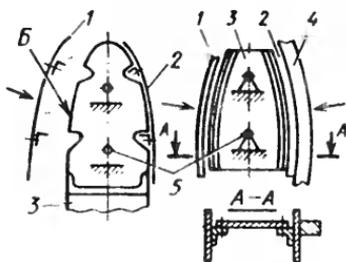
Сборка с базированием по поверхности каркаса:
